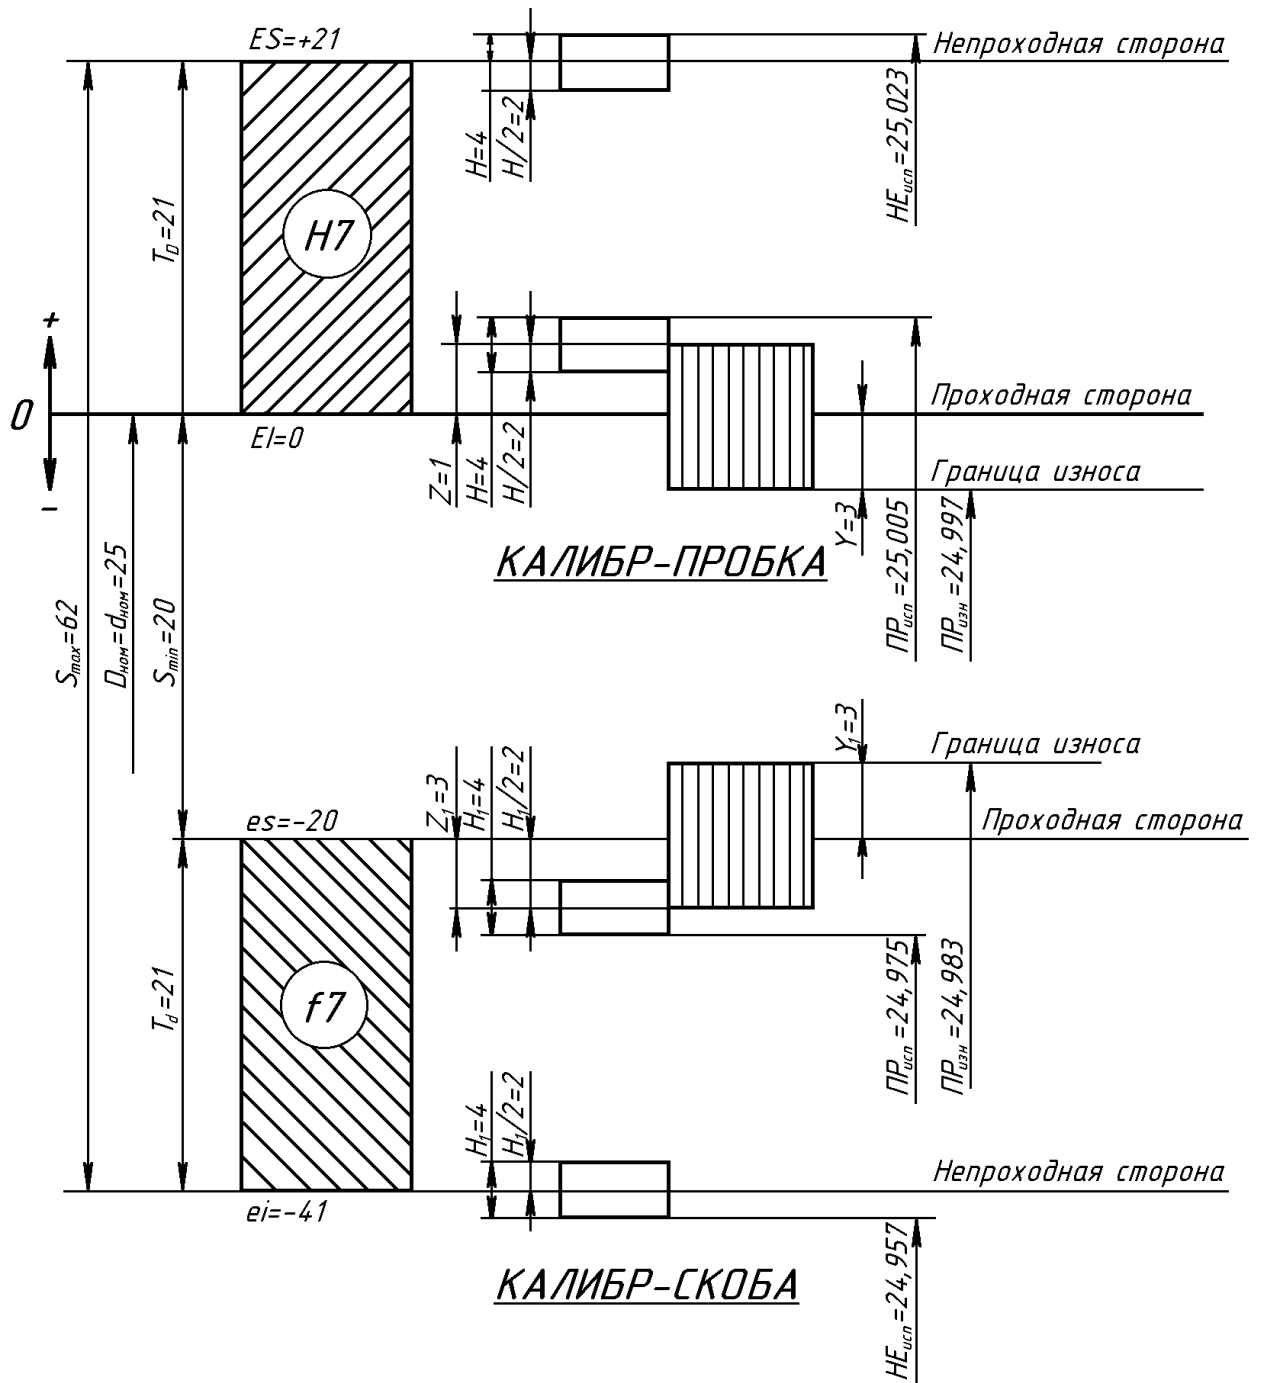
Схема расположения полей допусков калибров
